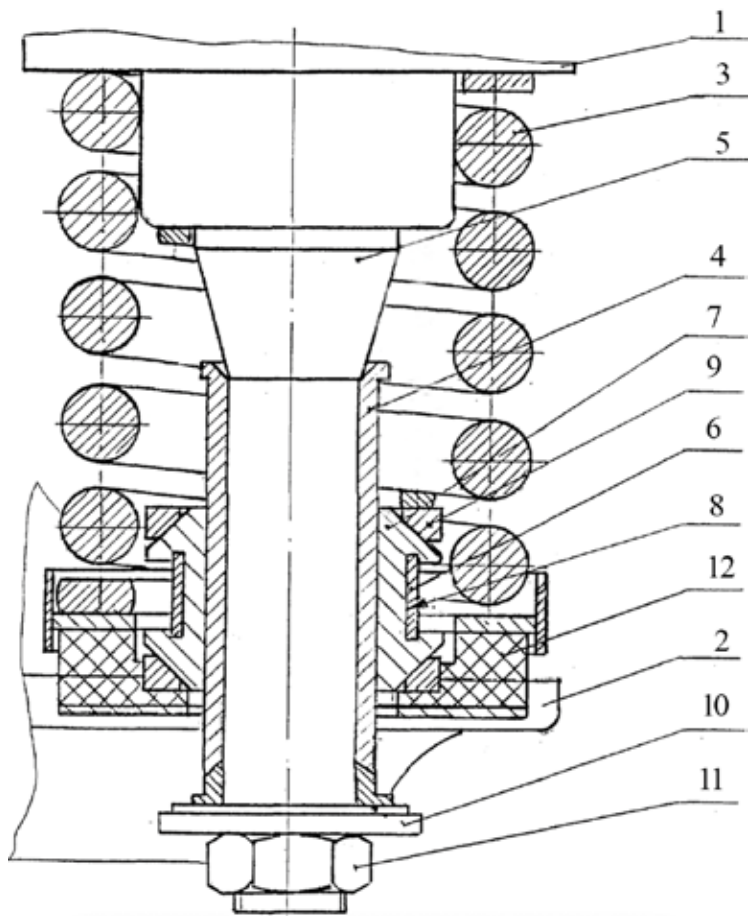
Шпигонный узел вагона метрополитена: 1 – защитный колпак; 2 – резиновая прокладка; 3 – нижняя опора пружины; 4 – пластмассовая втулка; 5 – крепежная проволока; 6 – пружина; 7 – верхняя направляющая опора; 8 – шпигтон; 9 – стопорная планка; 10 – винт; 11 – фиксирующая гайка; 12 – защитный кожух; 13 – гайка; 14 – нижняя опора пружины; 15 – резиновая втулка; 16 – стяжной хомут<sup>3</sup>.
